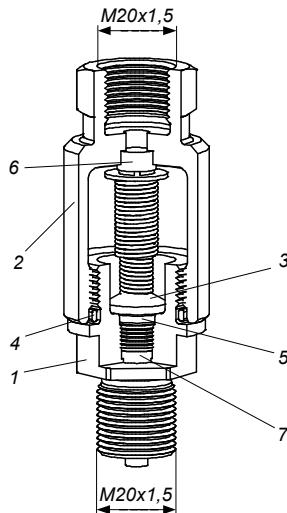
Устройство гасителя колебаний давления ГСК250Мс-1Б1Г: 1 – корпус; 2 – крышка; 3 – демпфирующая вставка; 4, 5 – уплотнительное кольцо; 6, 7 – фильтр.
